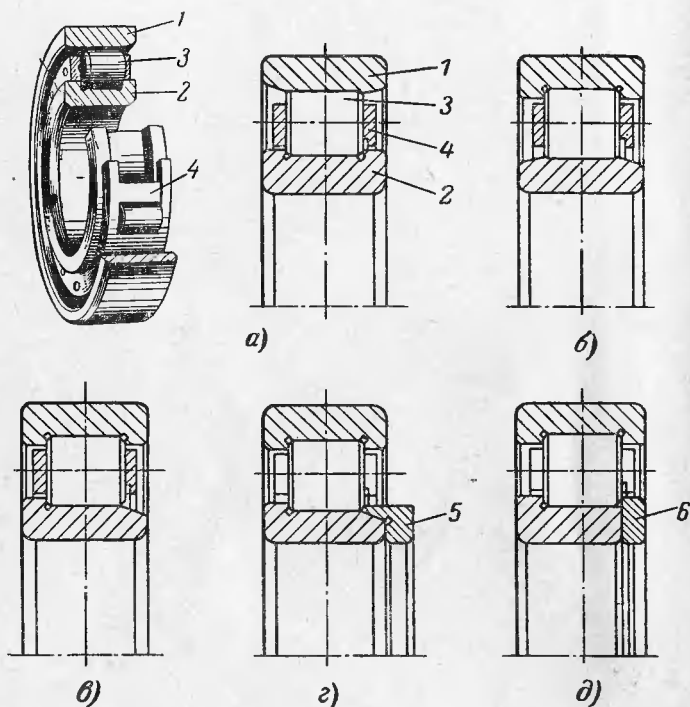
Роликовые радиальные однорядные подшипники с короткими цилиндрическими роликами.
